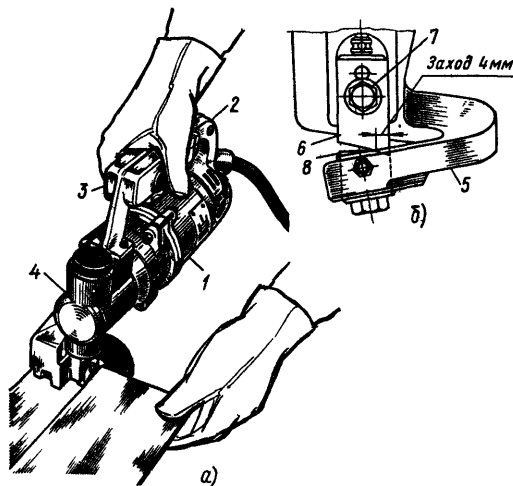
Резка электрическими ножницами: а — приемы резания ножницами С-434, б — схема ножниц; 1 — электродвигатель, 2 — рукоятка, 3 — выключатель, 4 — редуктор, 5 — скоба, 6 — верхний нож, 7 — эксцентрик, 8 — нижний нож
